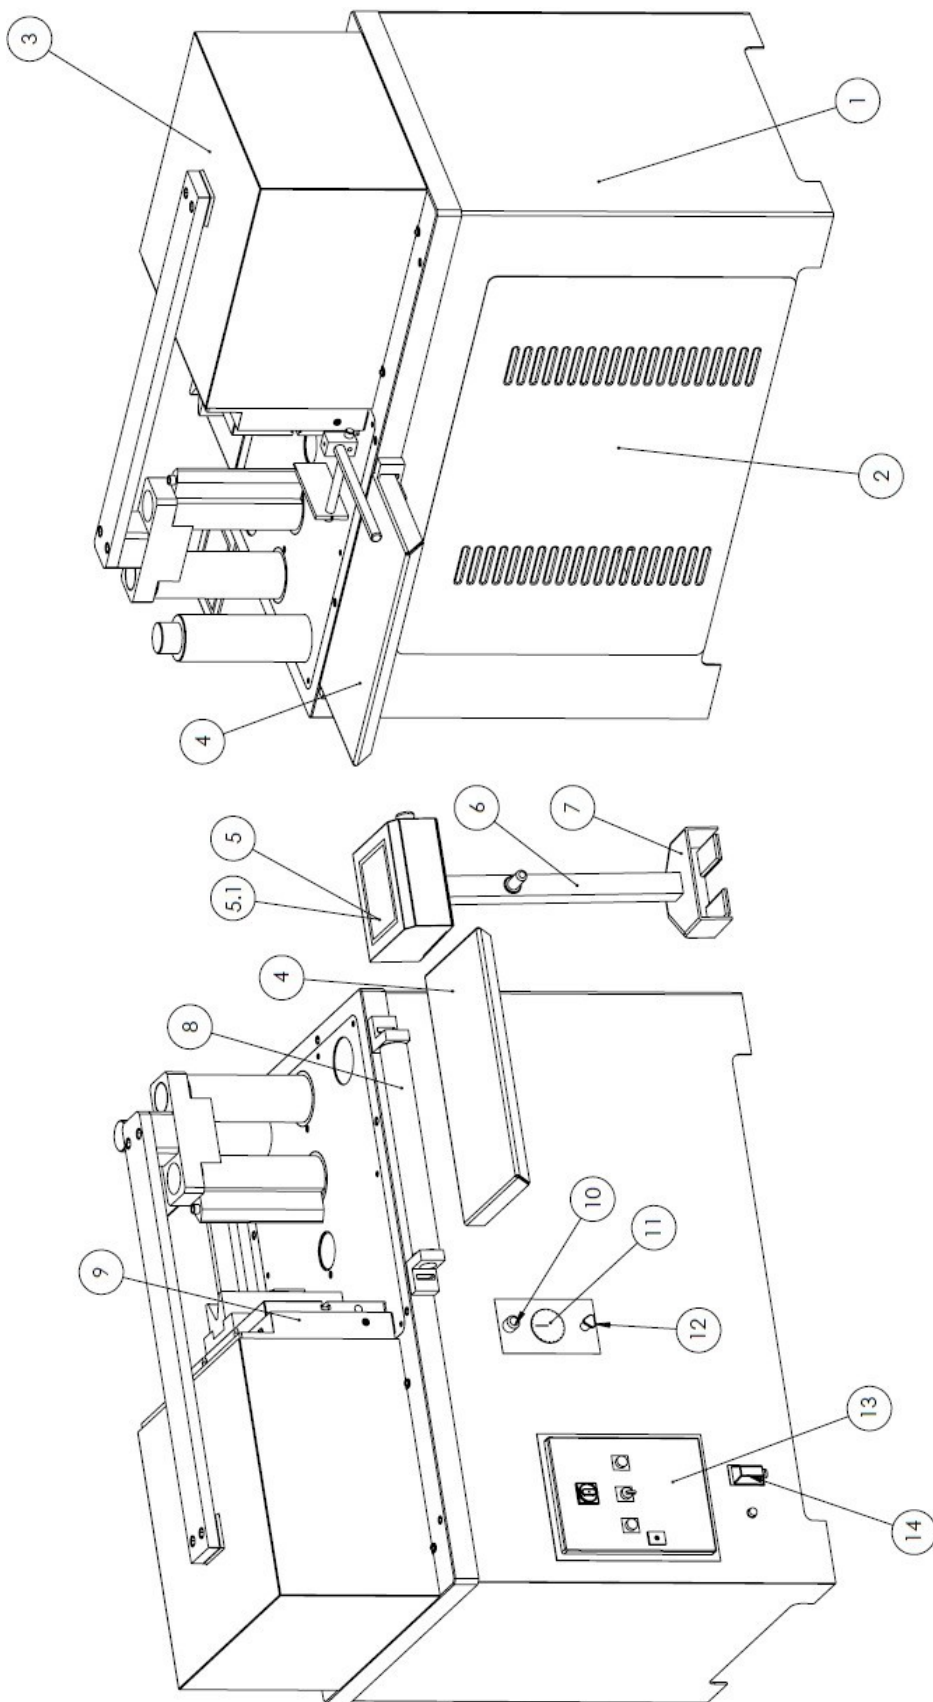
Schéma des pièces 1 Machine complète HBP 80 ou HBP 100
